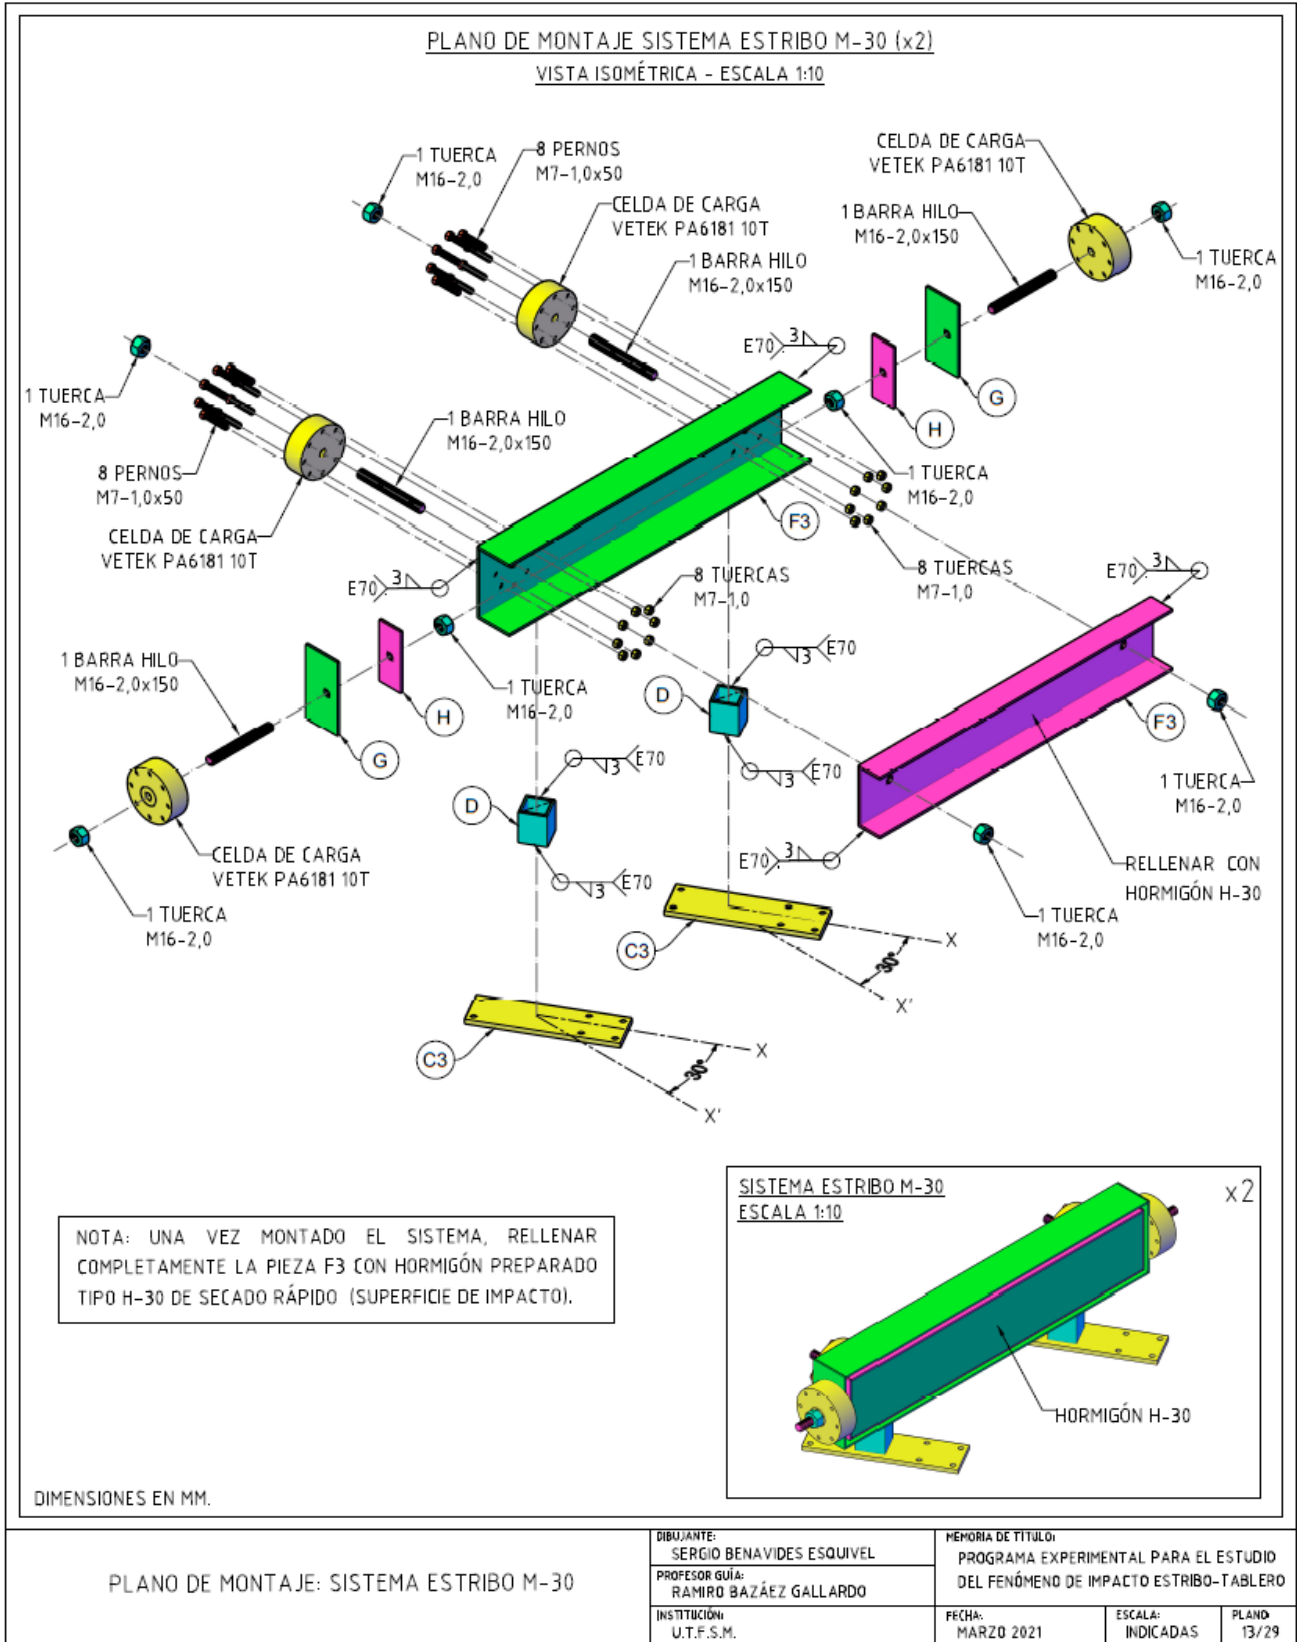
Plano de Montaje: Sistema Estribo M-30.
